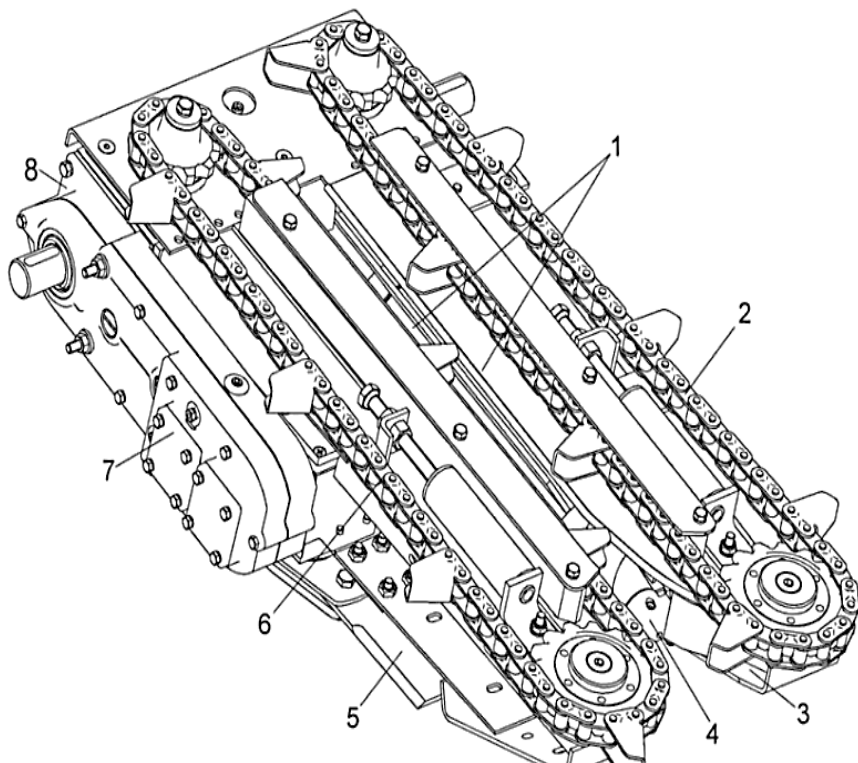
Русло: 1 – отрывочные пластины; 2, 6 – подающие цепи с захватами; 3 – рама русла; 4 – стеблепротягивающие вальцы; 5 – ротор с ножами; 7 – редуктор привода ротора
